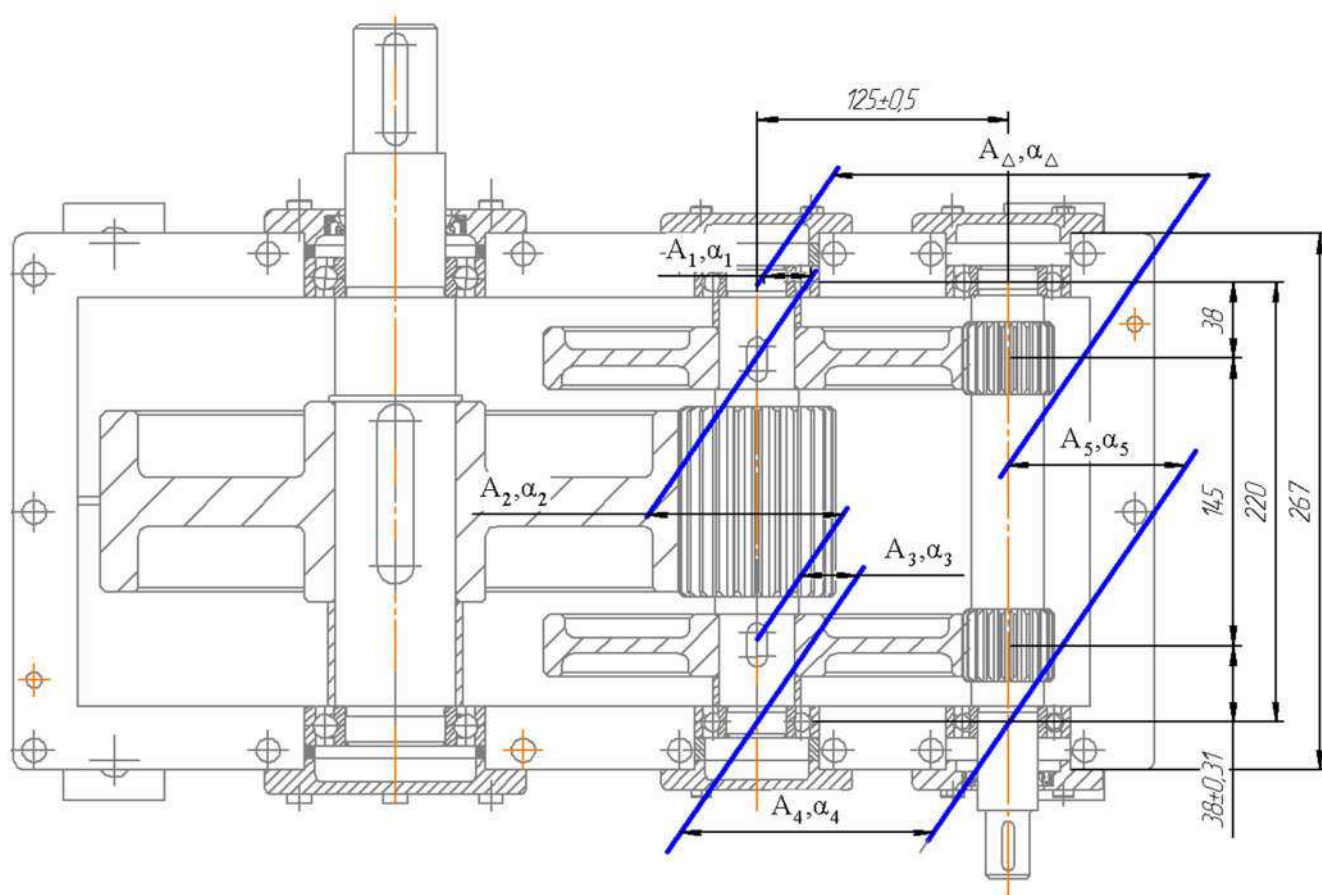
Размерная цепь цилиндрической зубчатой передачи (быстроходная)
